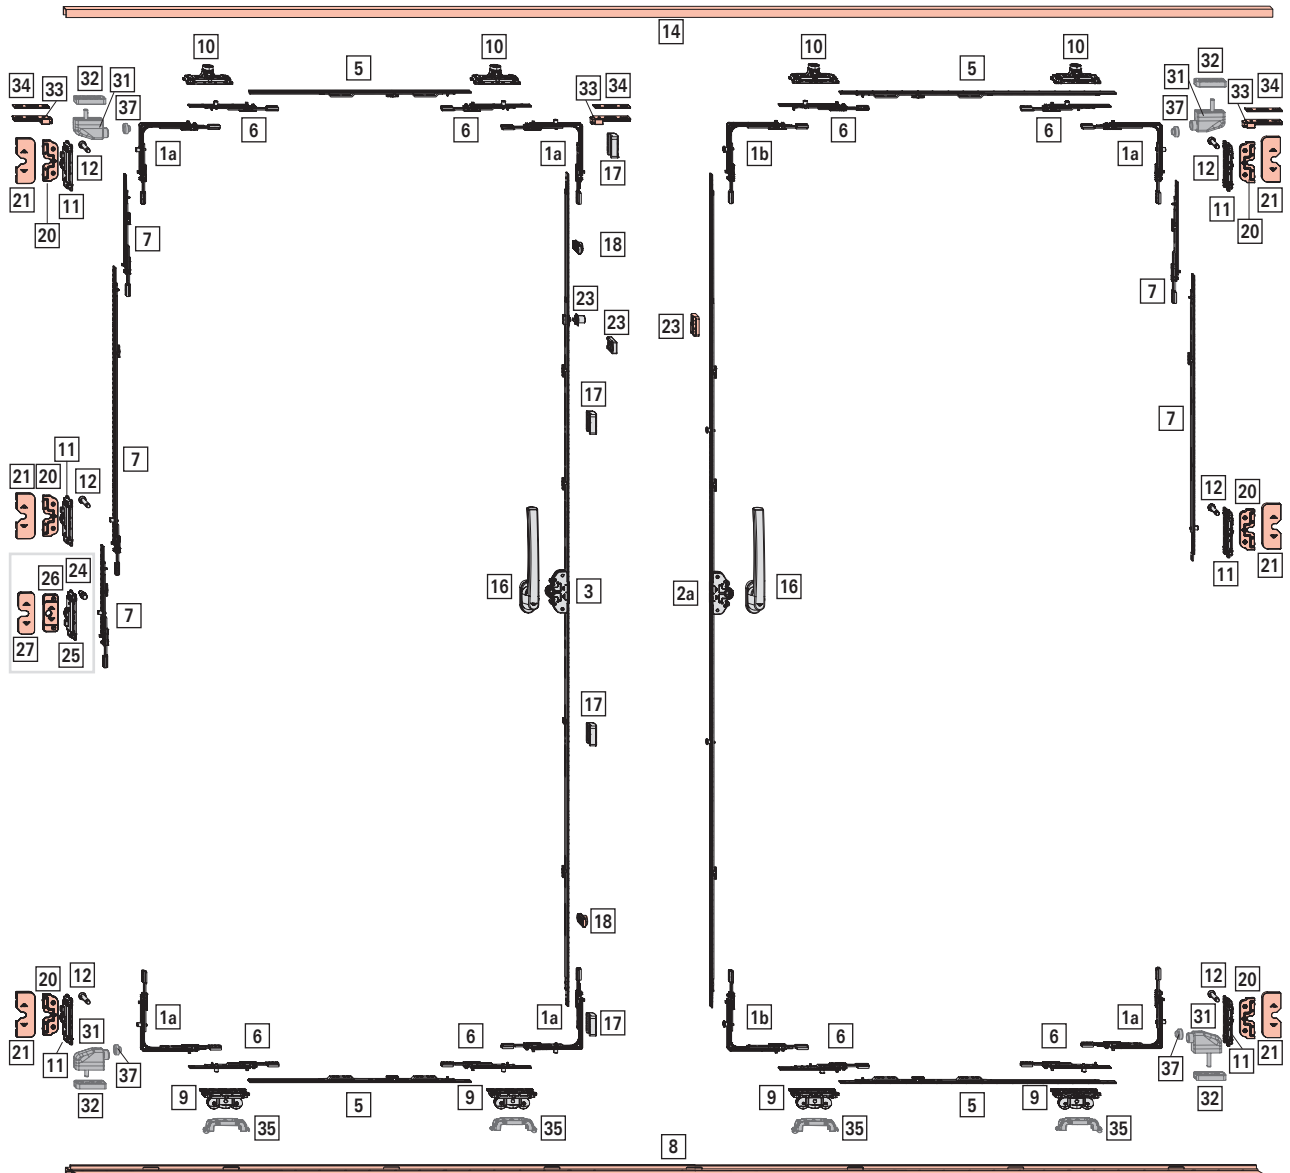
abgebildet: Holz; Ausführung: erstöffnender Flügel DIN L, zweitöffnender Flügel DIN R; FFB 900 mm; FFH 1900 mm; Getriebe DM 35
